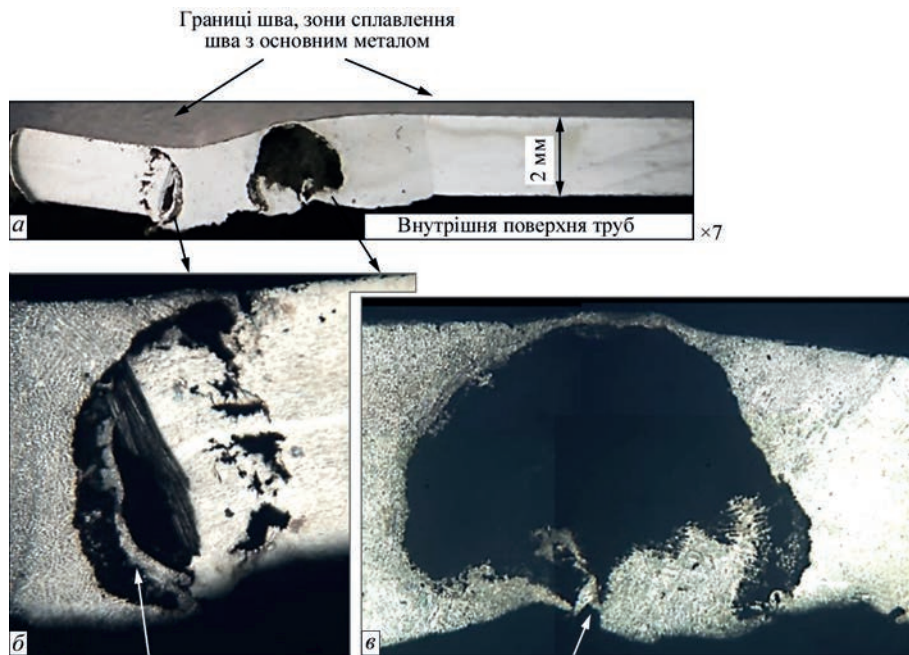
Наскрізні дефекти у шві: а – поперечний переріз зразка, ×7; б – несплавлення шва з основним металом, корозія, ×27; в – непровар кореня шва, корозія металу шва у порожнині з боку внутрішньої поверхні, ×27
